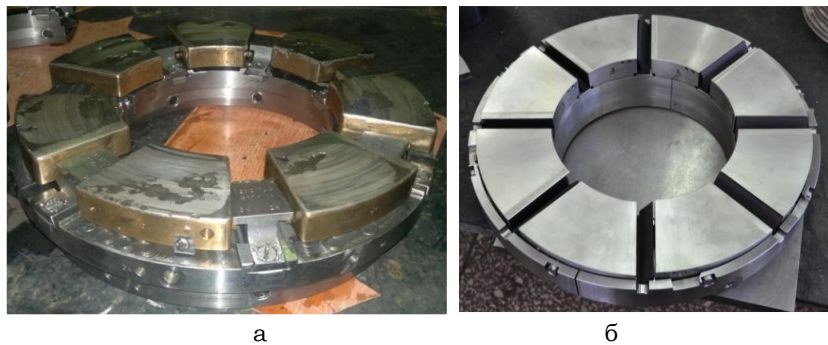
Штатный подшипник (а) и подшипник TRIZ® (б)
